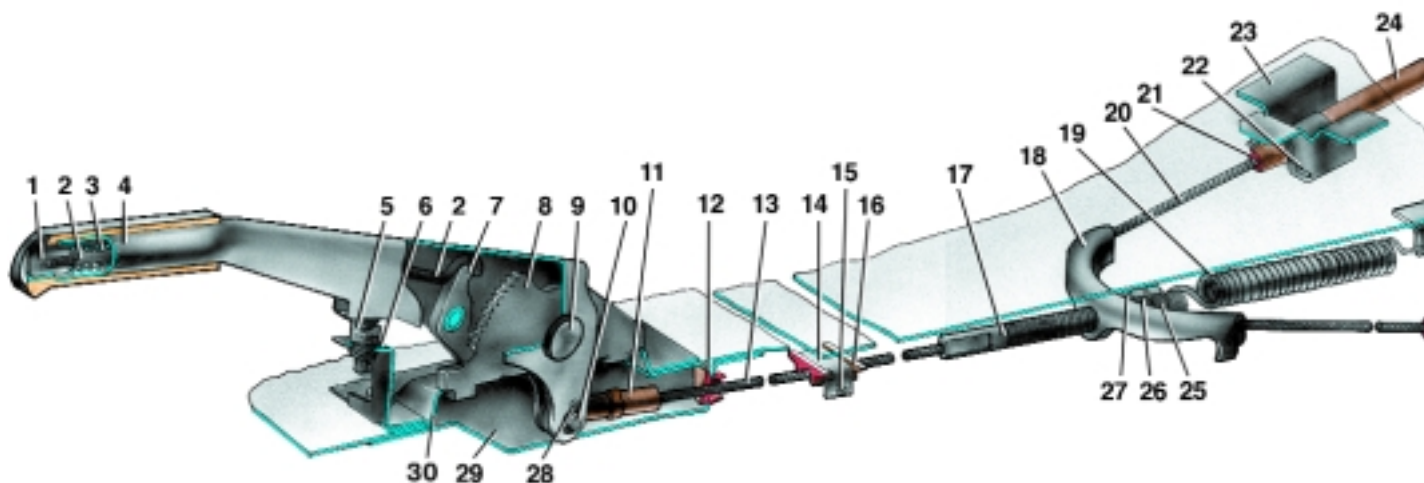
Привод стояночной тормозной системы: 1 – кнопка; 2 – тяга собачки; 3 – пружина; 4 – рычаг стояночного тормоза; 5 – включатель контрольной лампы; 6 – кронштейн включателя; 7 – собачка; 8 – сектор; 9 – ось; 10 – палец; 11 – передний наконечник переднего троса; 12 – втулка; 13 – передний трос; 14 – кронштейн; 15 – шплинт; 16 – вкладыш; 17 – задний на-
